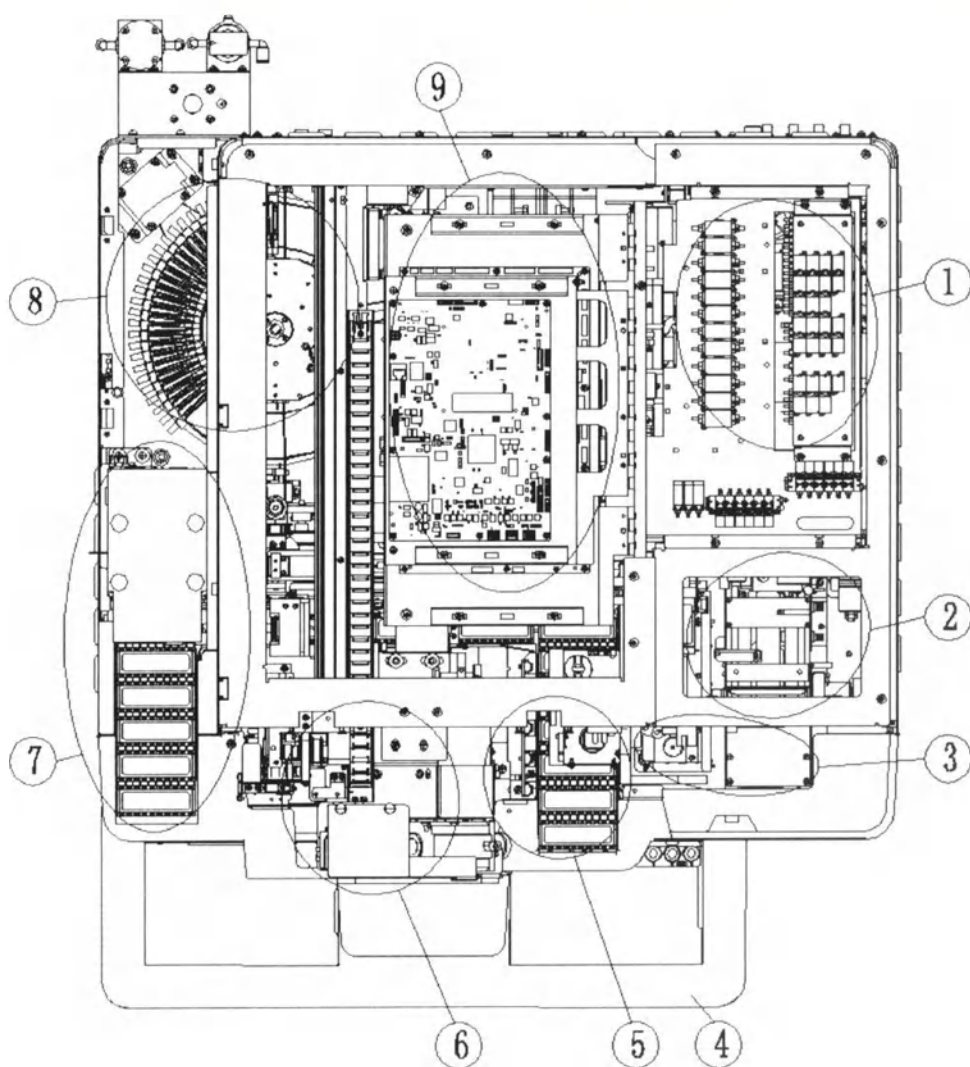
Вид основного блока сверху (верхняя крышка открыта)
